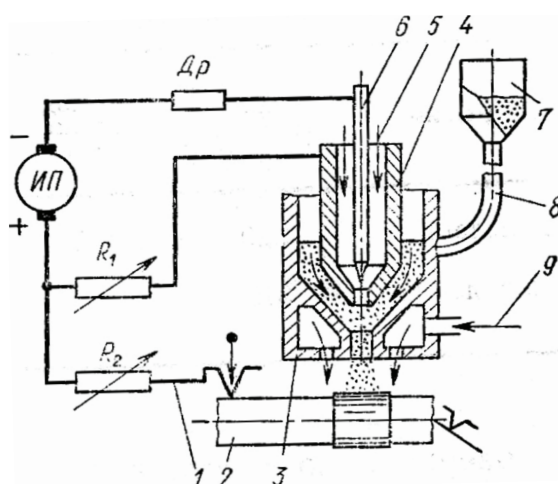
Восстановление изношенных валов наплавкой: 1-станок; 2-восстанавливаемый вал; 3-наружное сопло плазмотрона; 4 – медное сопло; 5 – плазмо-образующий газ; 6 – вольфрамовый катод; 7 – питатель для подачи порошка; 8 – транспортирующий газ; 9-защитный газ; ИП – источник электрического питания; R1 и R2 – реостаты; Др – дроссель
